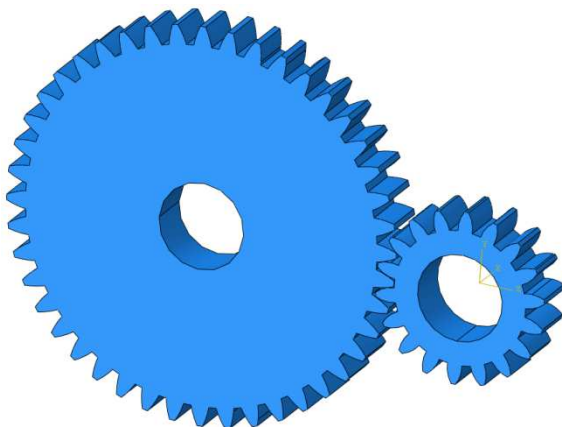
Geometria koła walcowego o zarysie ewolwentowym
